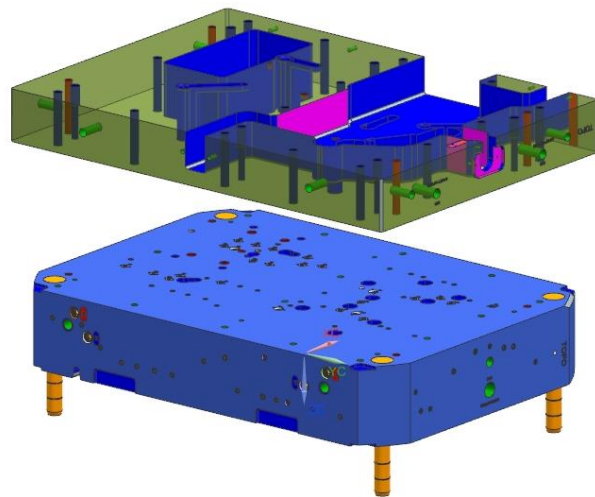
Montagem da placa de alojamento do sistema de injeção
